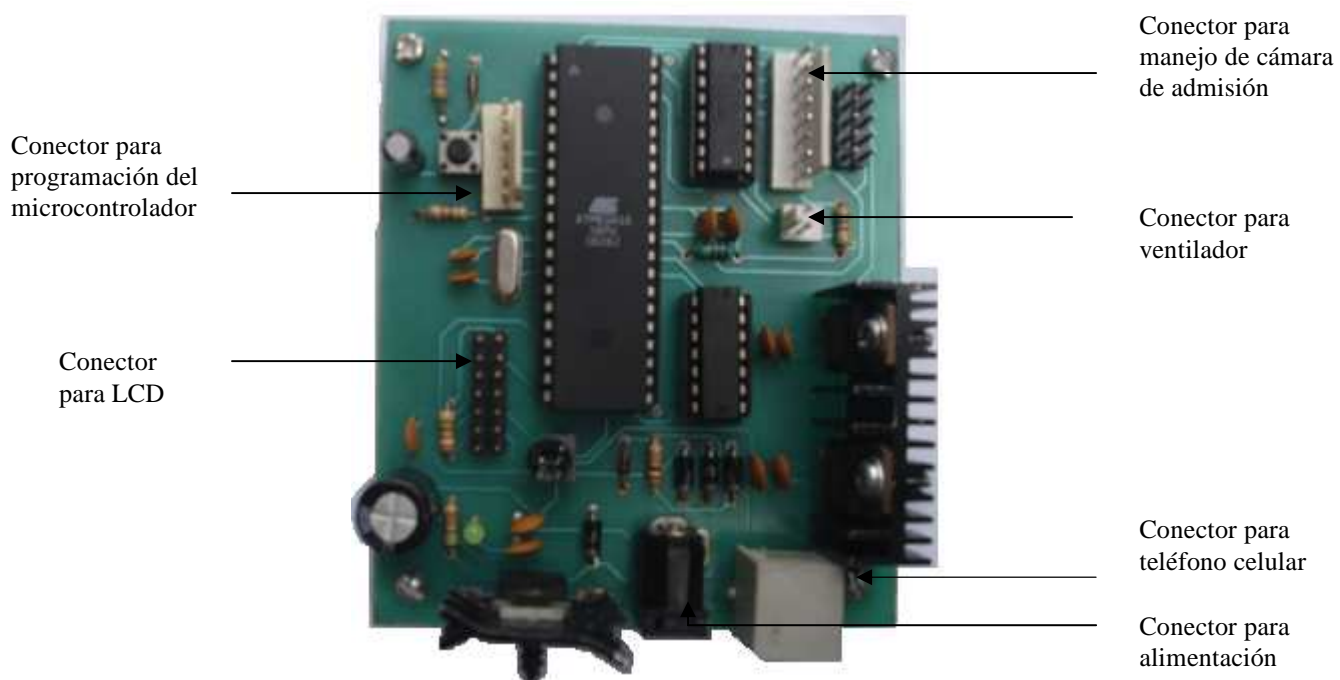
Elementos soldados en la Placa No.1
